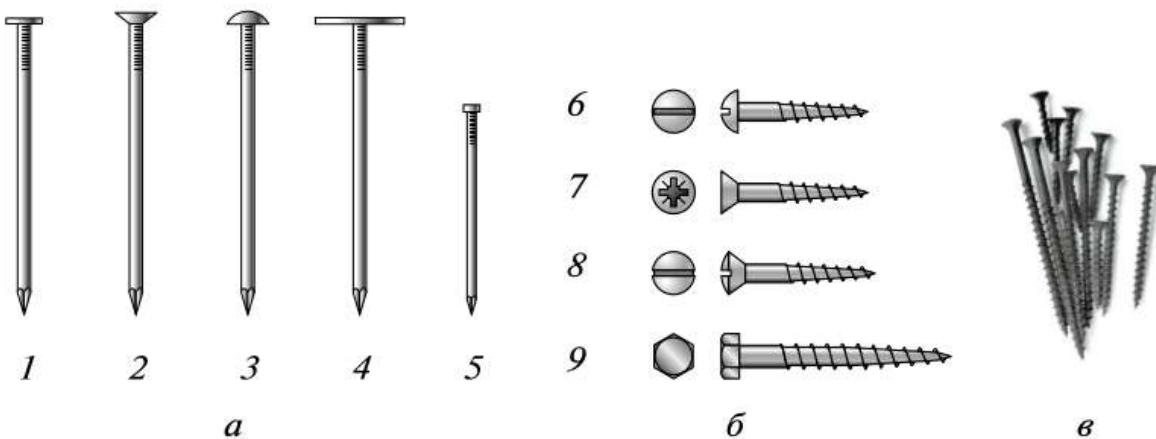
Крепёжные изделия для соединения деталей из древесины:
